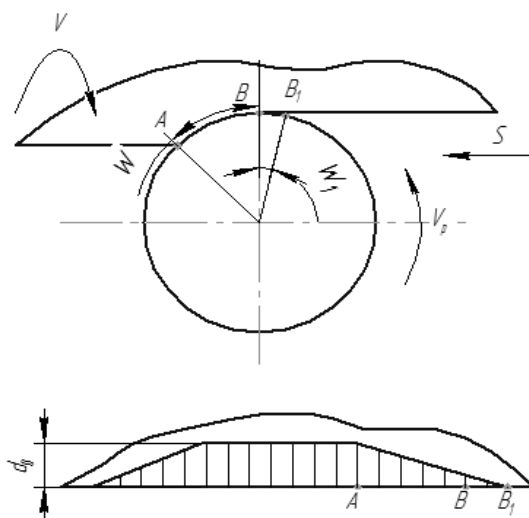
Схема работы и характер износа режущей кромки чашечного резца с непрерывным обновлением
